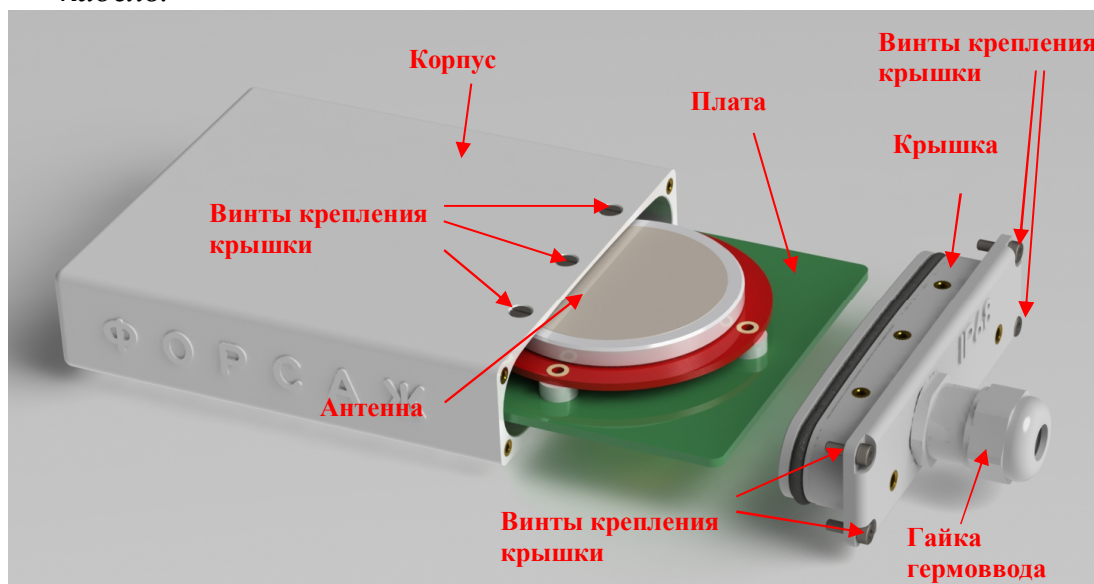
Снятие крышки и вытягивание платы из корпуса модуля
